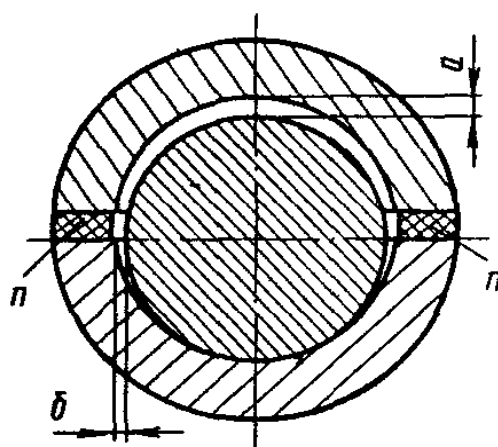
Зазоры между валом и вкладышем подшипника
